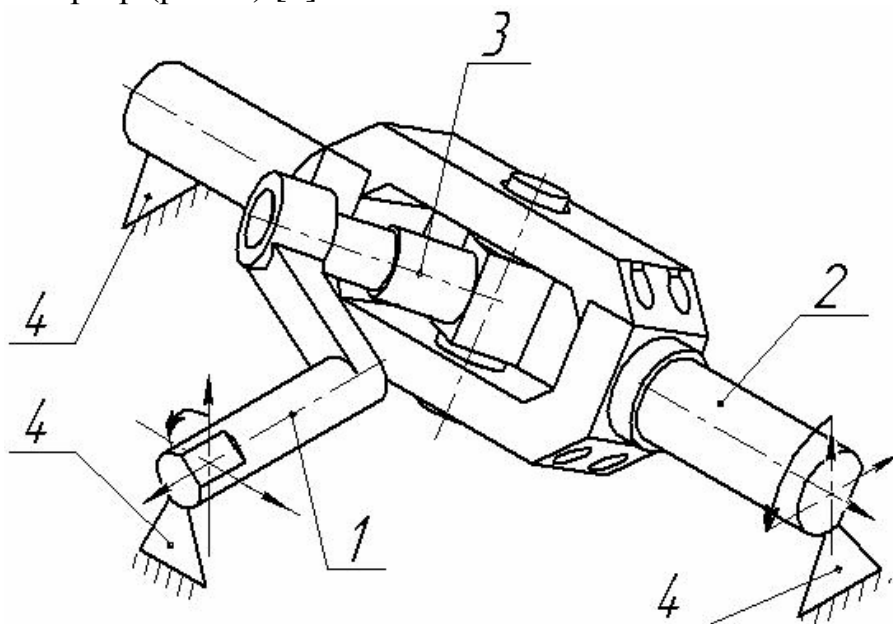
Просторовий шарнір: 1- кривошип; 2 – хрестовина; 3 – хитний вал; 4 – опора
